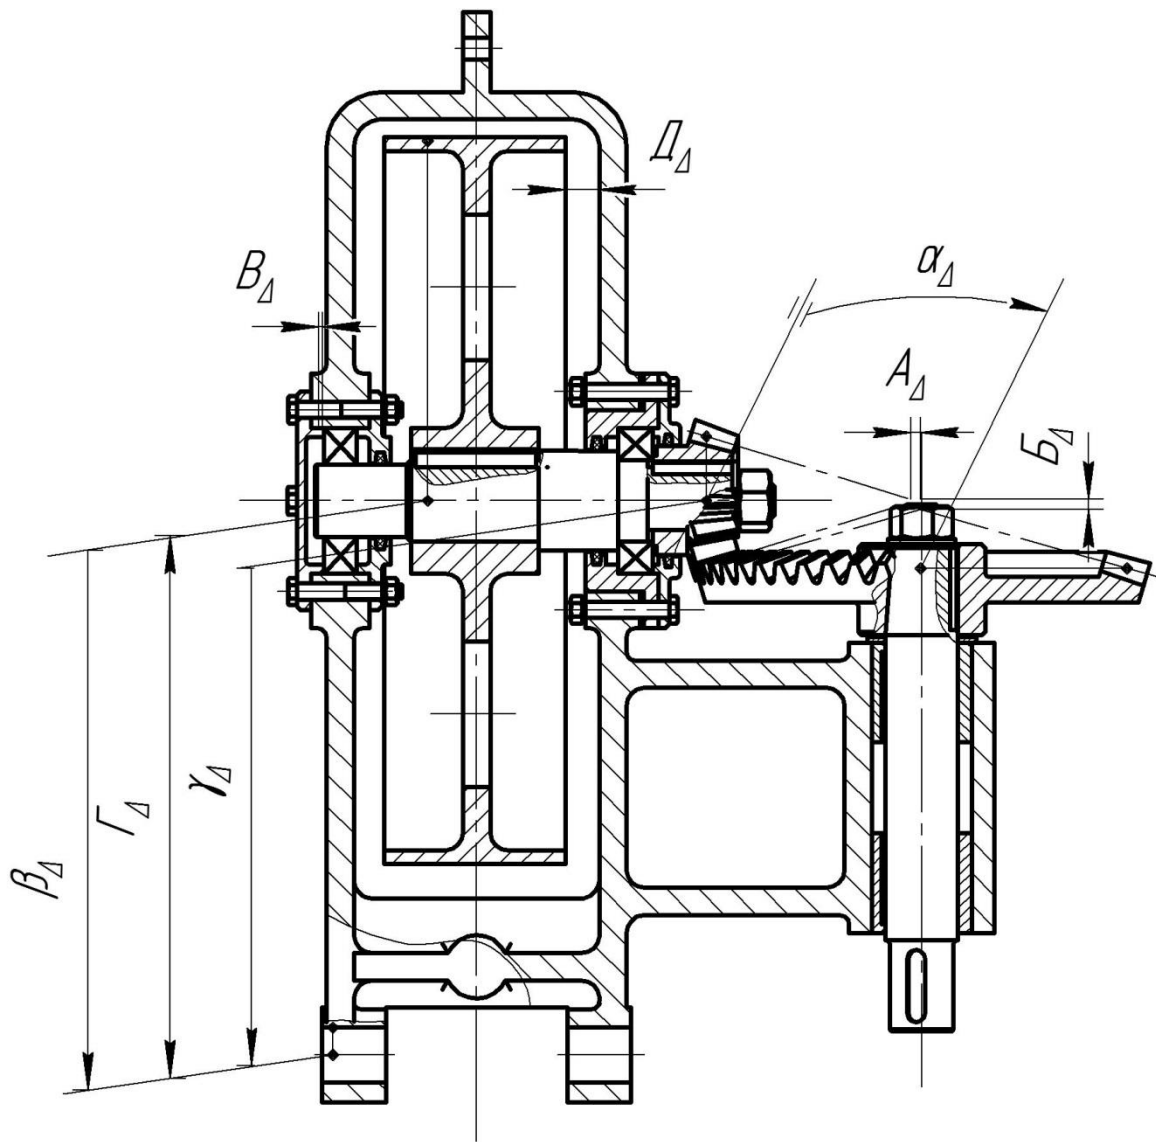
Ескіз редуктор акутового із виявленими замикаючими ланками
